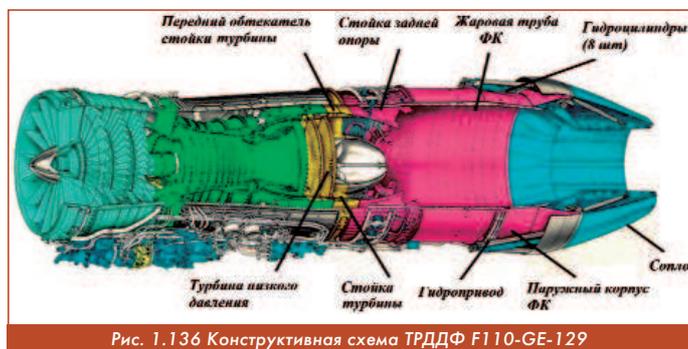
Конструктивная схема ТРДДФ F110-GE-129
